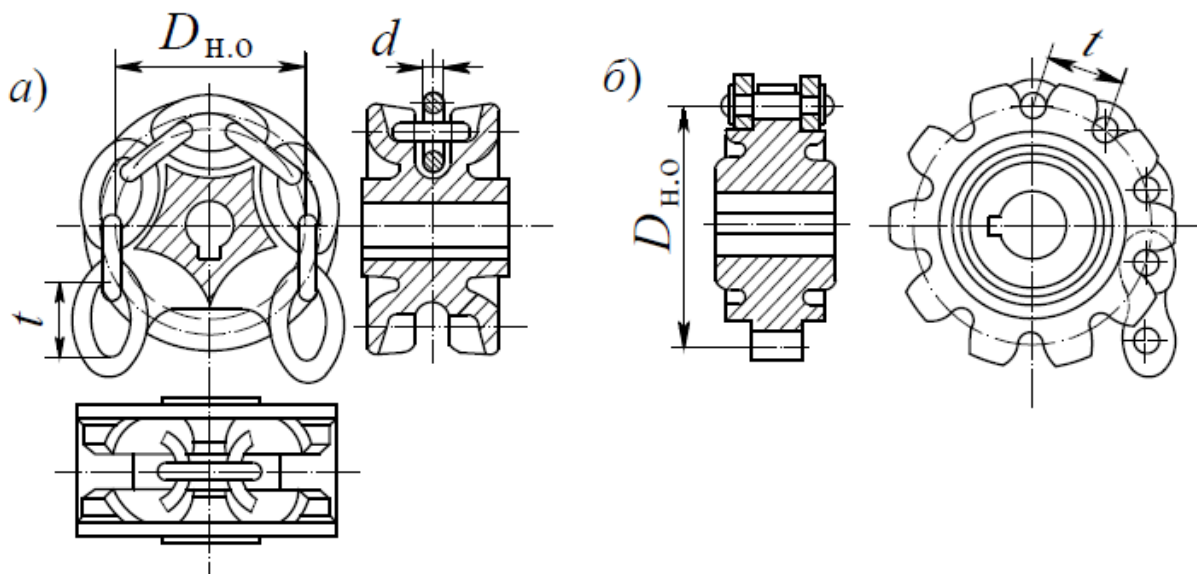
Звездочки: *а* – для сварной цепи; *б* – для пластинчатой цепи
